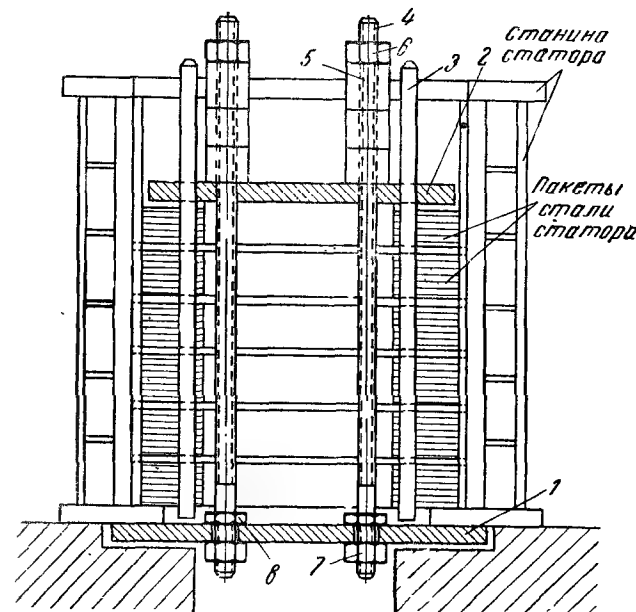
Установка статора и расположение приспособлений для прессовки стали.
